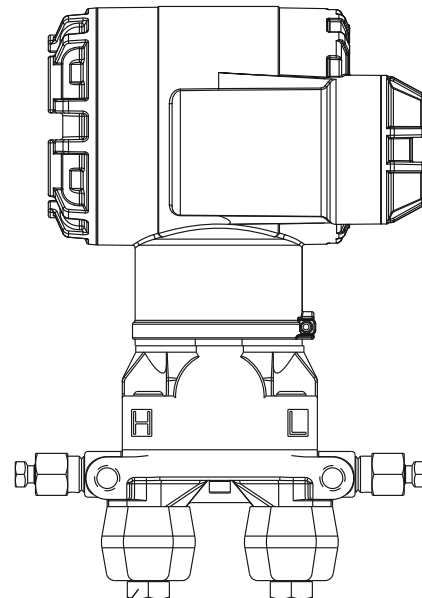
Parafusos de montagem e configurações de parafusos para flange Coplanar
